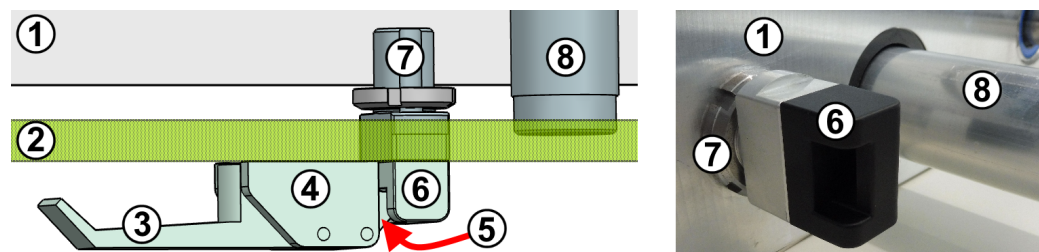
Querschnitts-Ansicht des Kniehebelspannmechanismus von oben (links) und Detailbild (rechts)
